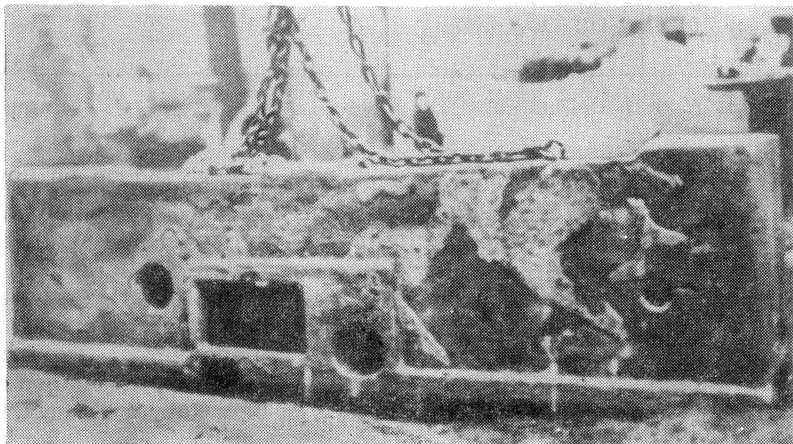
Ужимины и пригар на поверхности станины шлифовального станка.
